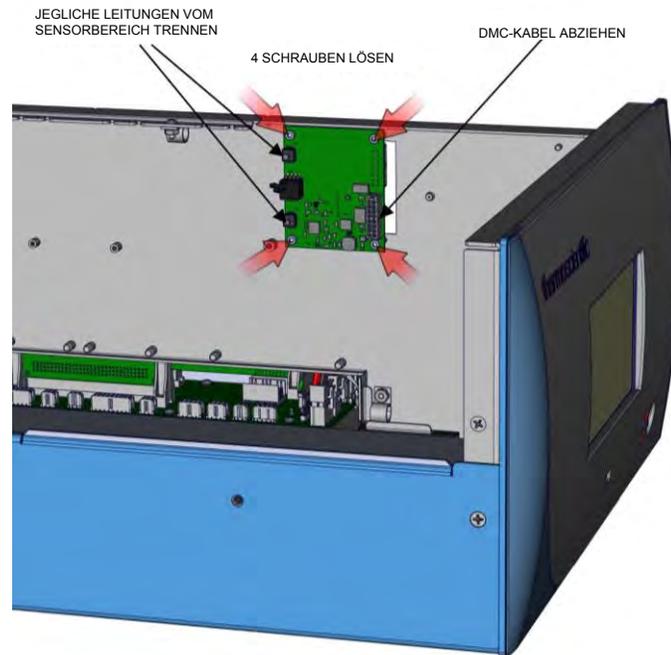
Druck- und Durchfluss-Platine, Schrauben
